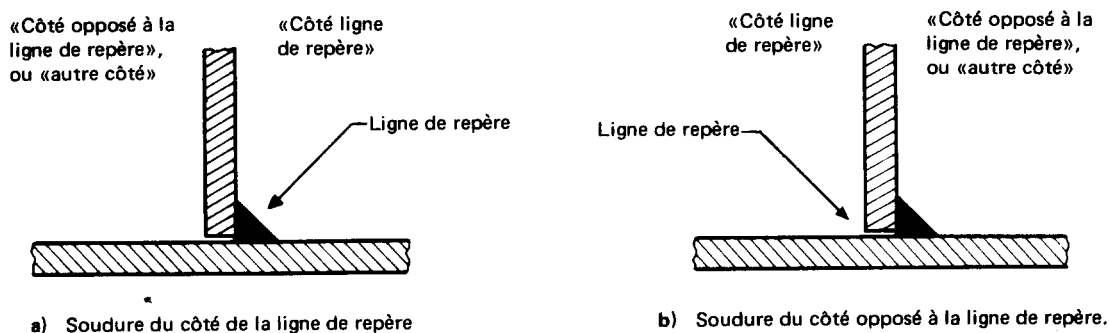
Assemblage en T avec une soudure d’angle
